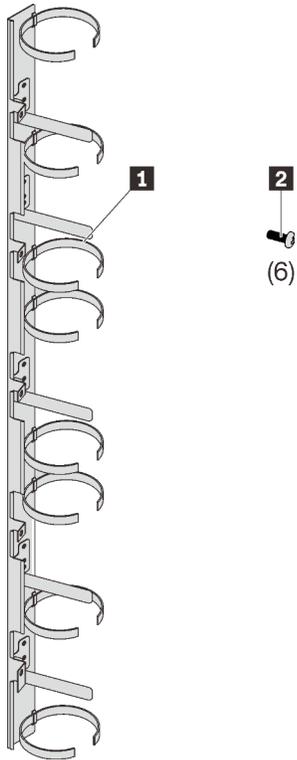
Componentes do suporte de gerenciamento de cabos frontais 21U
